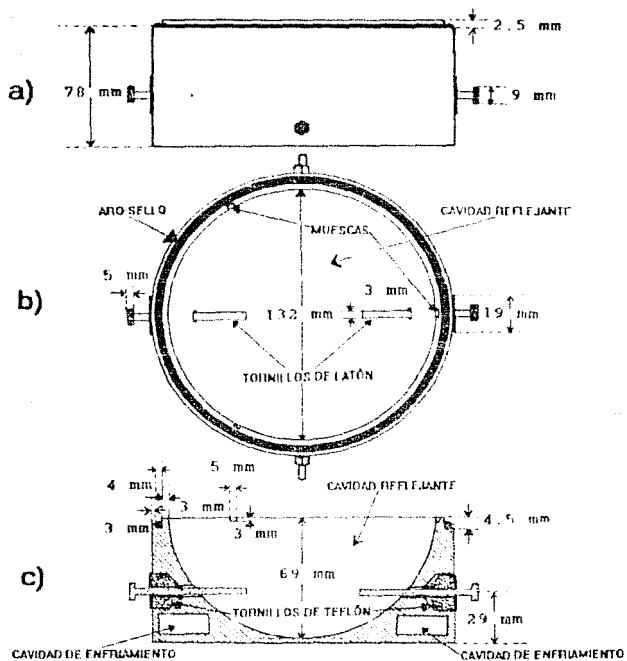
Sección interior del horno a) vista lateral, b) vista por arriba y c) corte longitudinal.
